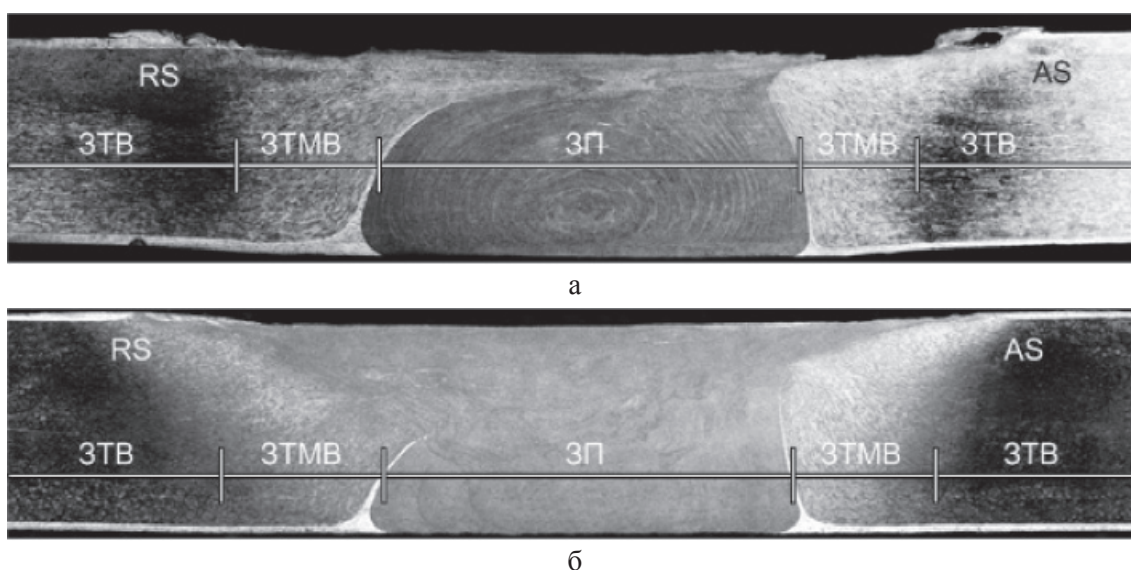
Макрофотографии сварных соединений сплава Д16 на образцах 1 (а) и 2 (б)
